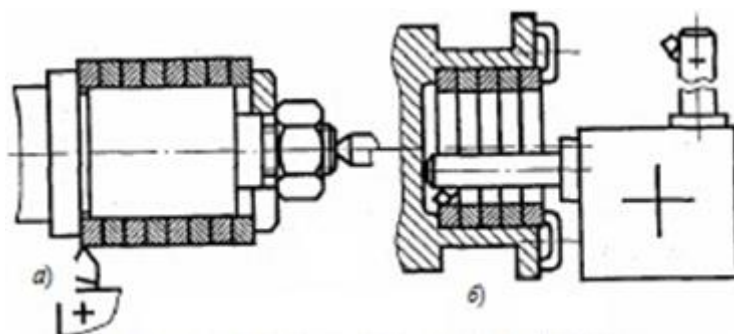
Многоместная последовательная обработка: а – одним; б – несколькими инструментами
